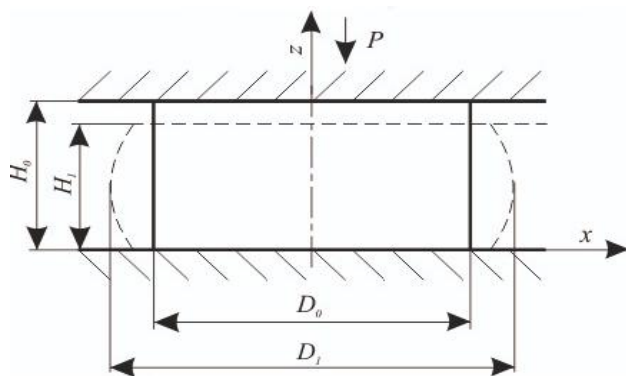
Схема осадки: H_0 , D_0 - начальные размеры заготовки, H_1 , D_1 - размеры заготовки после осадки
